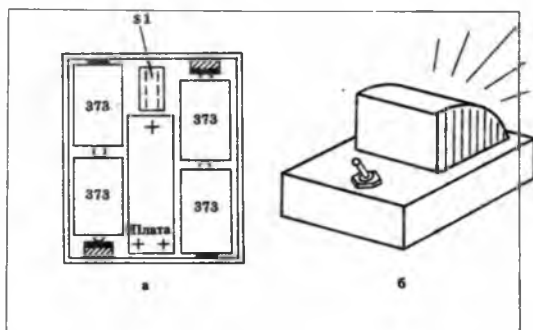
Аварийный мигающий фонарь: а — компоновка; б — внешний вид
